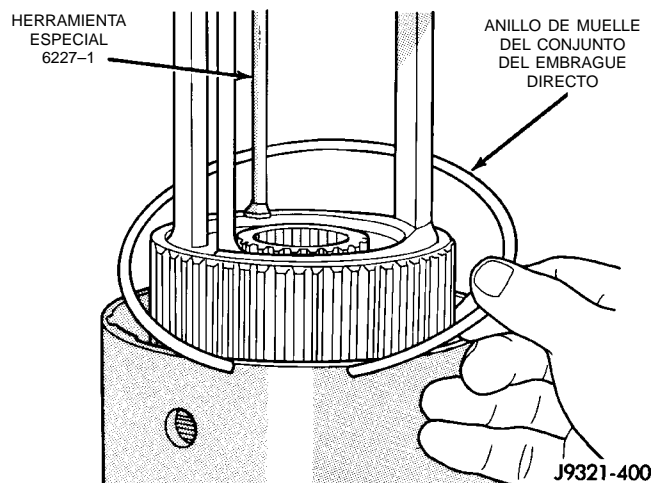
Instalación del anillo de muelle del conjunto del embrague directo
